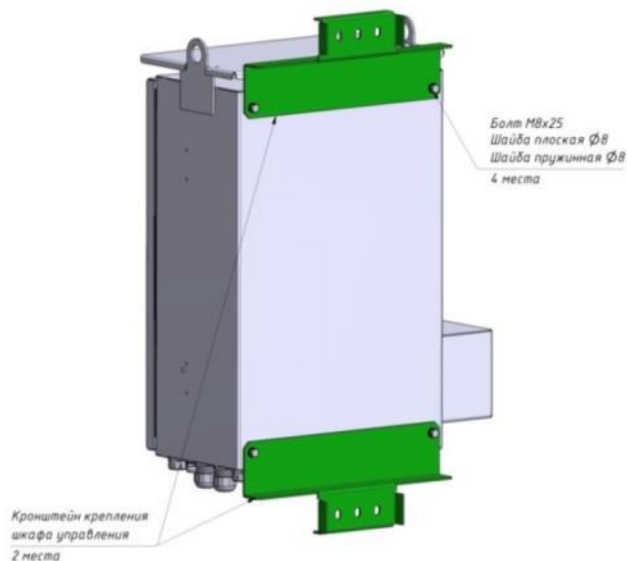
Установка присоединительных кронштейнов шкафа управления
